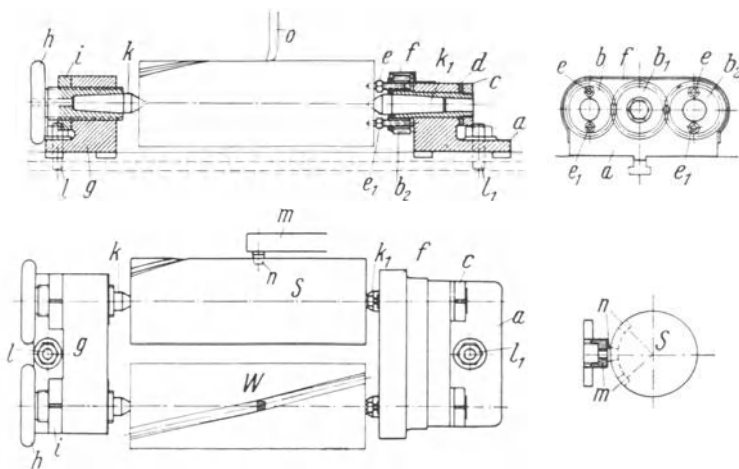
Kopier-Hobelvorrichtung für Drallnuten auf Zylindermäntel.
